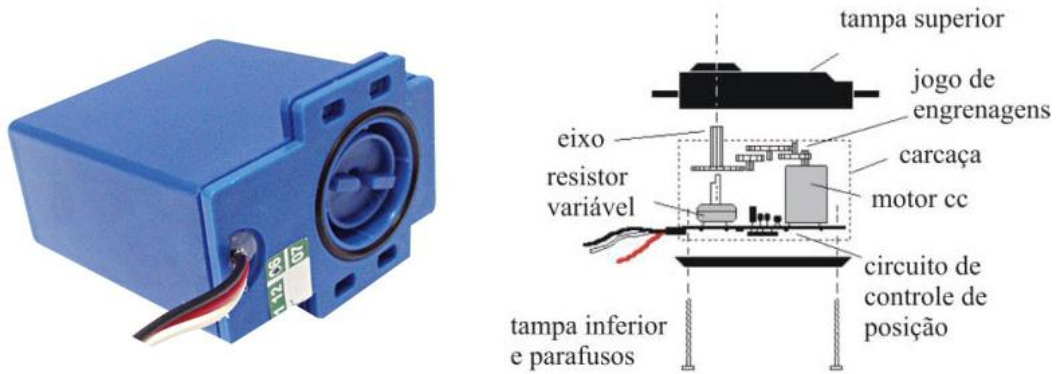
Fotografia e vista explodida do servo motor utilizado
